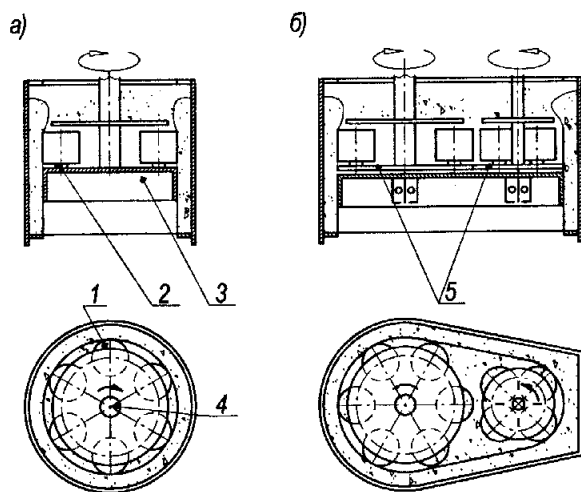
Нагнетатели сыпучих сред с роликовыми нагнетательными элементами для формования труб и колец:
